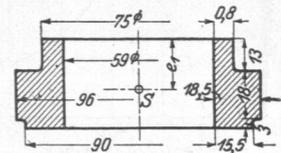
Querschnitt FB des Flansches Abb. 669.
